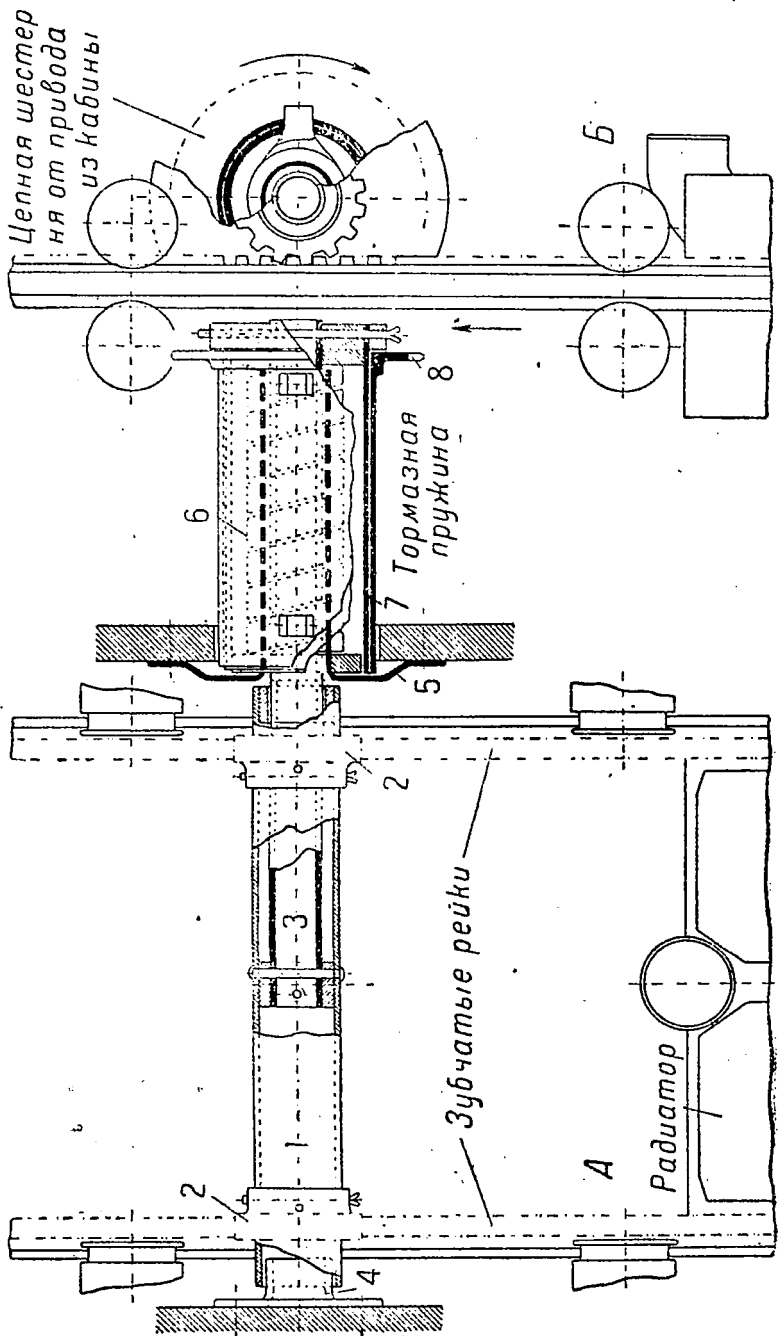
Подъемный механизм и стопорные муфты опускающегося радиатора: А—вид спереди; Б—вид сбоку; 1—основная труба подъемного механизма; 2—зубчатые шестерни; 3—внутренняя труба; 4,5— фляцы на упорных коробках; 6—стопорная пружина; 7—внутренняя муфта, соединенная с внутренней трубой; 8—ведущая шестерня.
